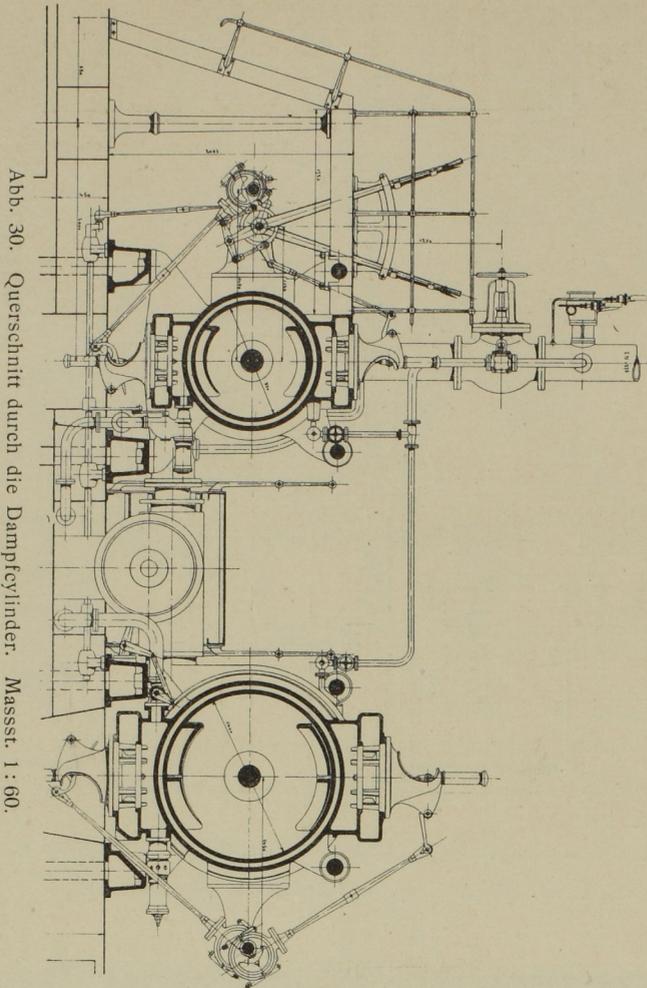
Querschnitt durch die Dampfzylinder. Massst. 1 : 60.
